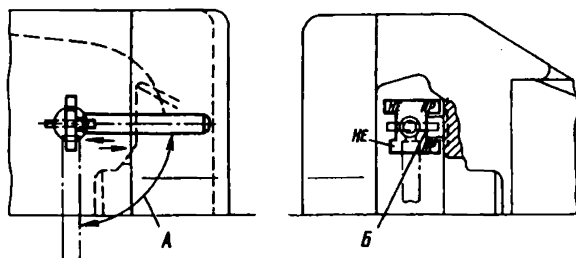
Проверка диаметра и состояния кромки торца шипа для замкодержателя шаблоном 806р
